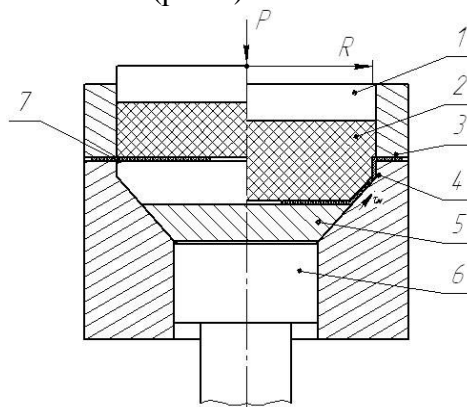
Схема формообразования тонкостенной детали из кольцевой заготовки:
